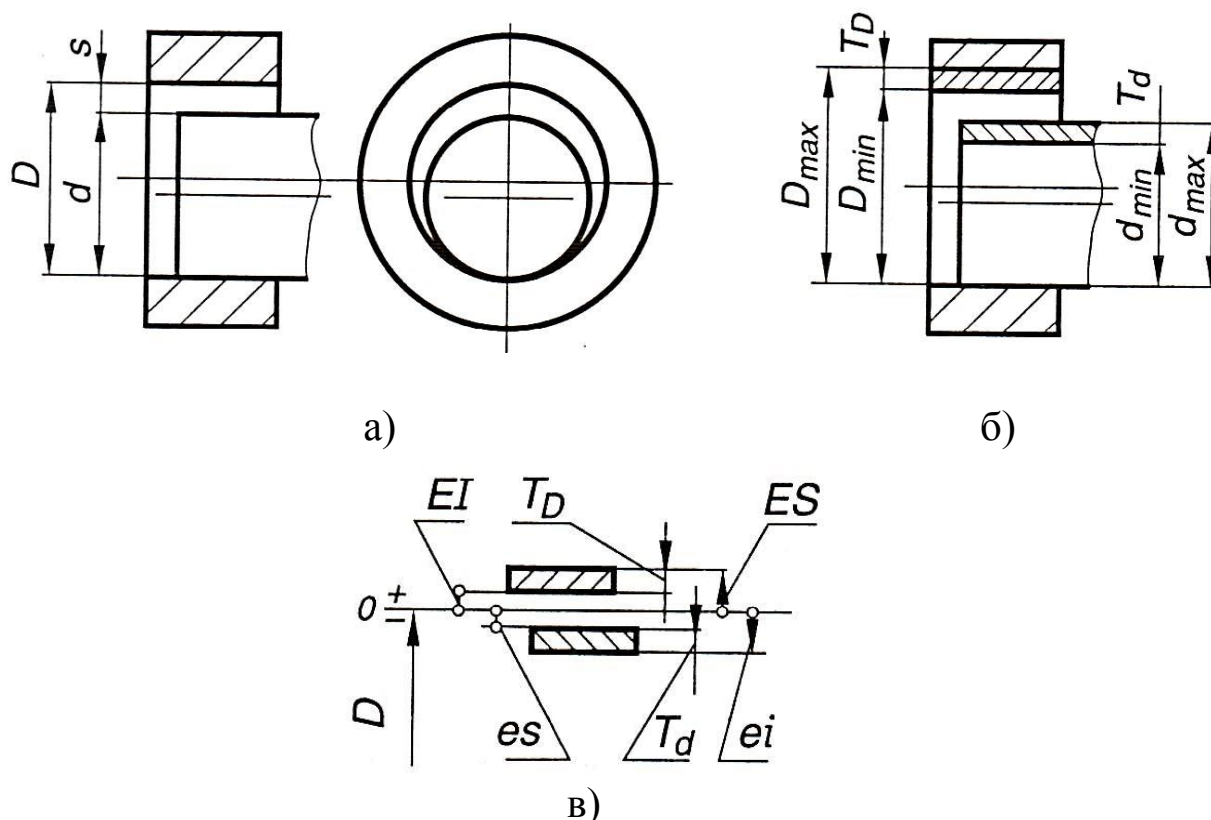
Схема расположения предельных размеров и полей допусков отверстия ( $T_D$ ) и вала ( $T_d$ ) в сопряжении с зазором ( $S$ )
